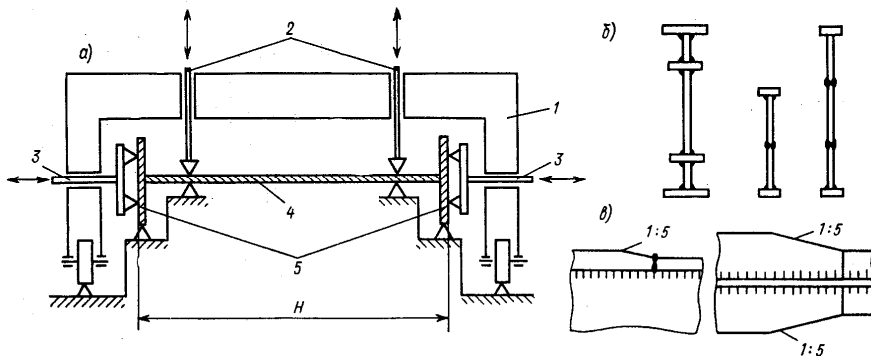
Схема самоходного портала для сборки двутавровых балок и конструктивное оформление двутавровых балок больших размеров
